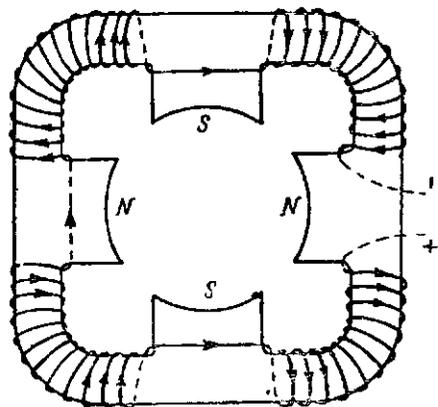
Схема приспособления для намагничивания ротора магнето Сцинтилла.
